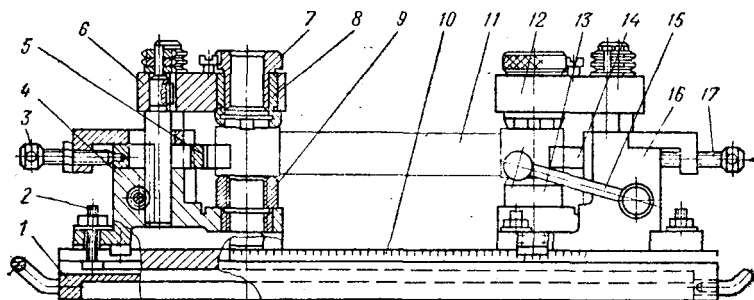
Универсально-наладочное приспособление для обработки отверстий в рычагах средних размеров
